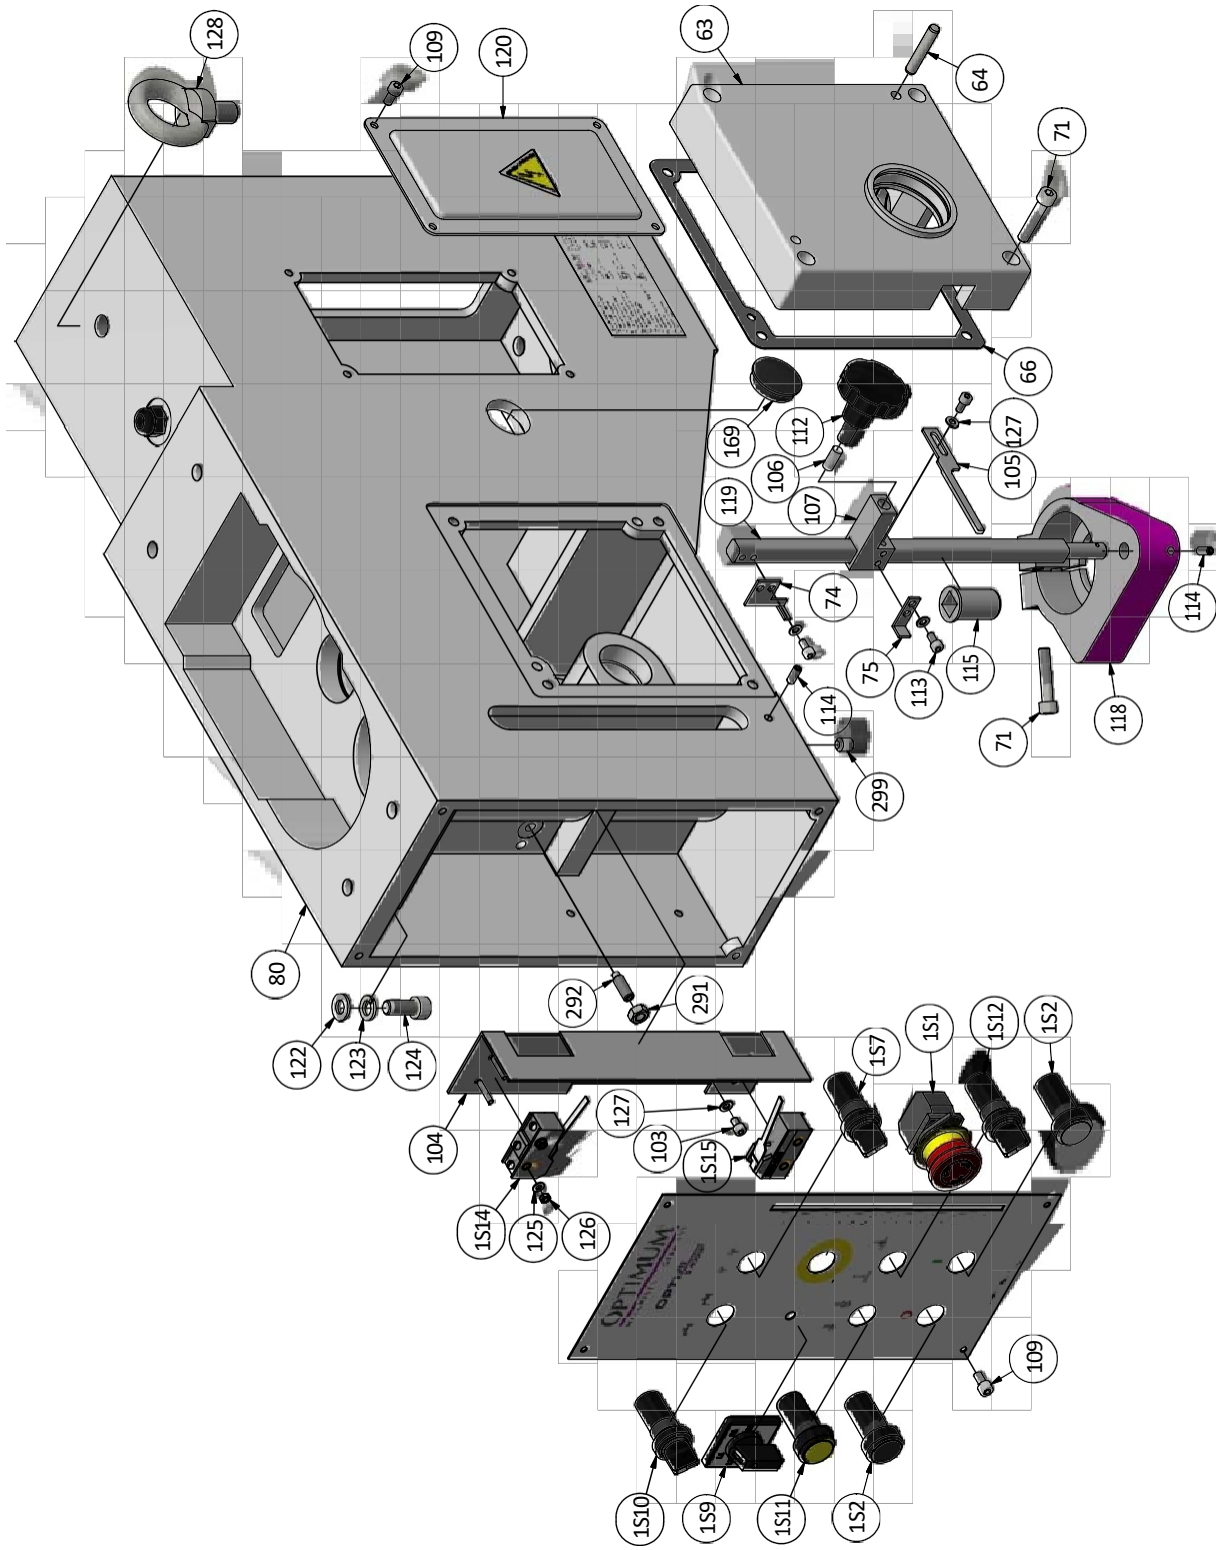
Vorschubgetriebe 3 von 4 - Gearbox 3 of 4
